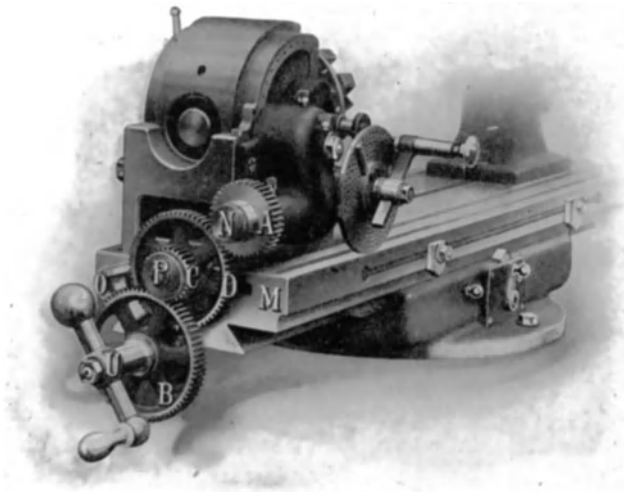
Ansicht des Wanderer-Universalteillapparates.
